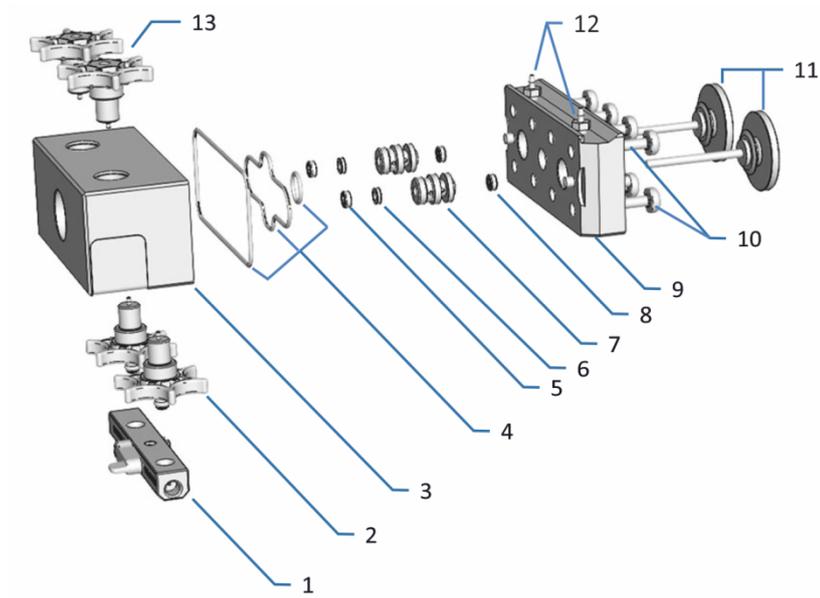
Vue d'ensemble des éléments de la tête de pompe
